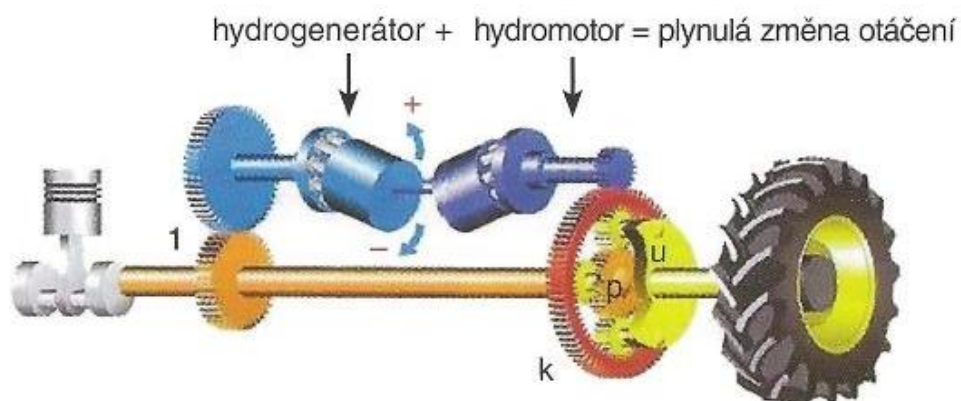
Základní koncepce používaných bezstupňových převodovek s hydrostatickou částí
